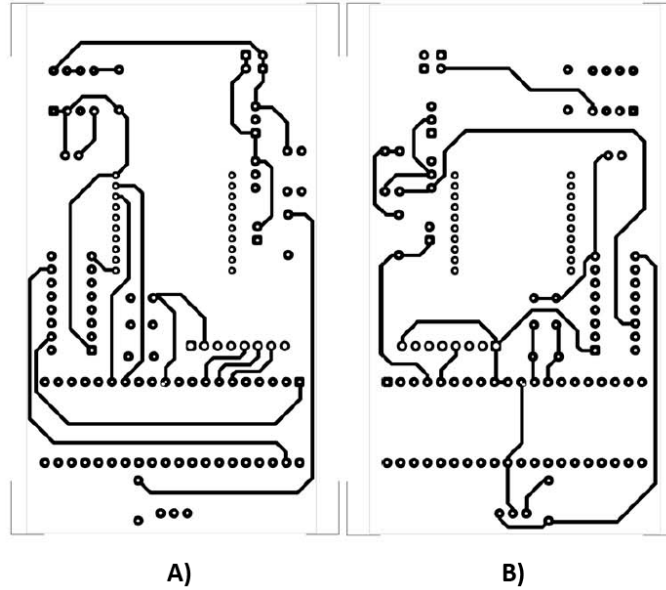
Patrones de PCB del módulo de sensores A) Cara posterior, B) Cara superior.
